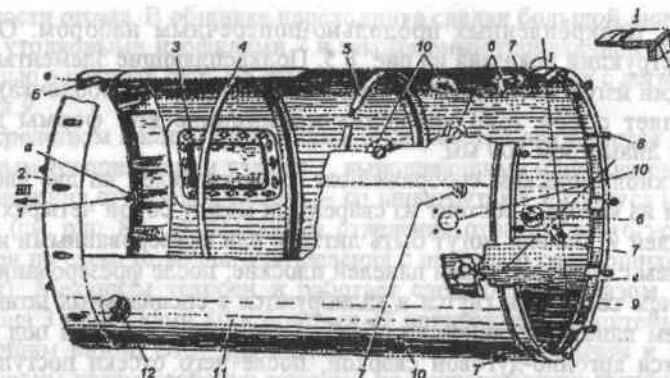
Конструкция сварного моноблочного отсека корпуса
